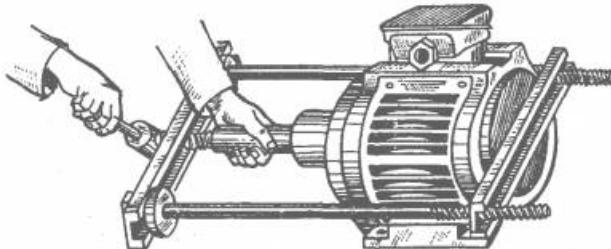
Насадка шкива на вал электродвигателя.
